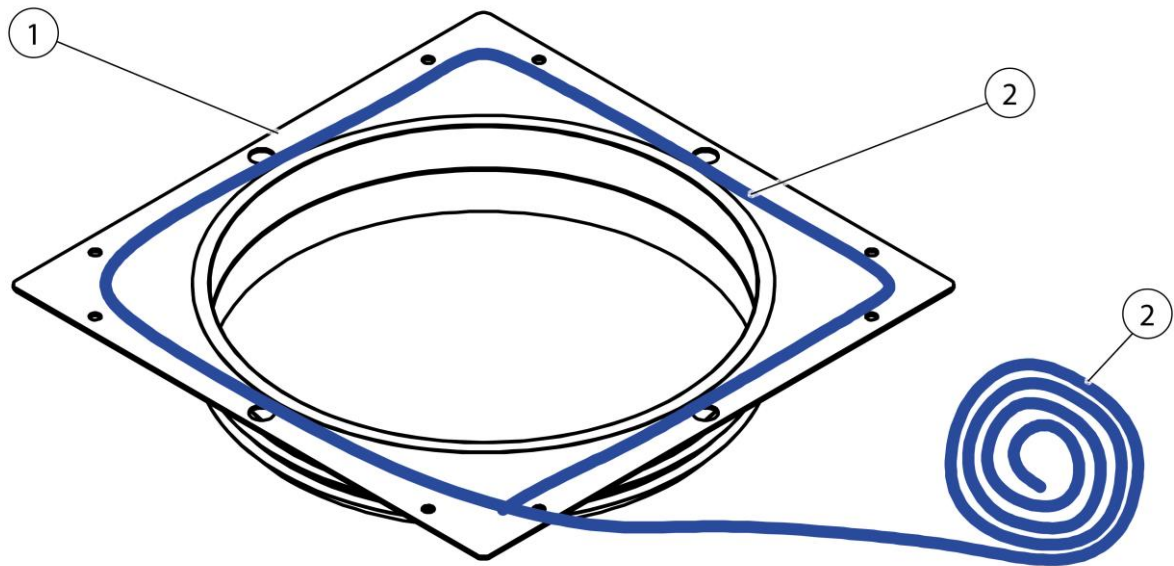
Монтаж – присоединительный патрубок, приклеивание уплотнительной ленты
